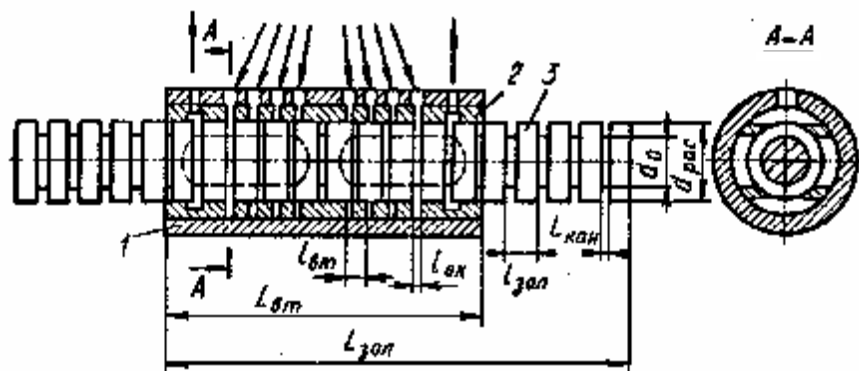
Конструктивная схема типовых элементов шагового распределителя поступательного движения:
